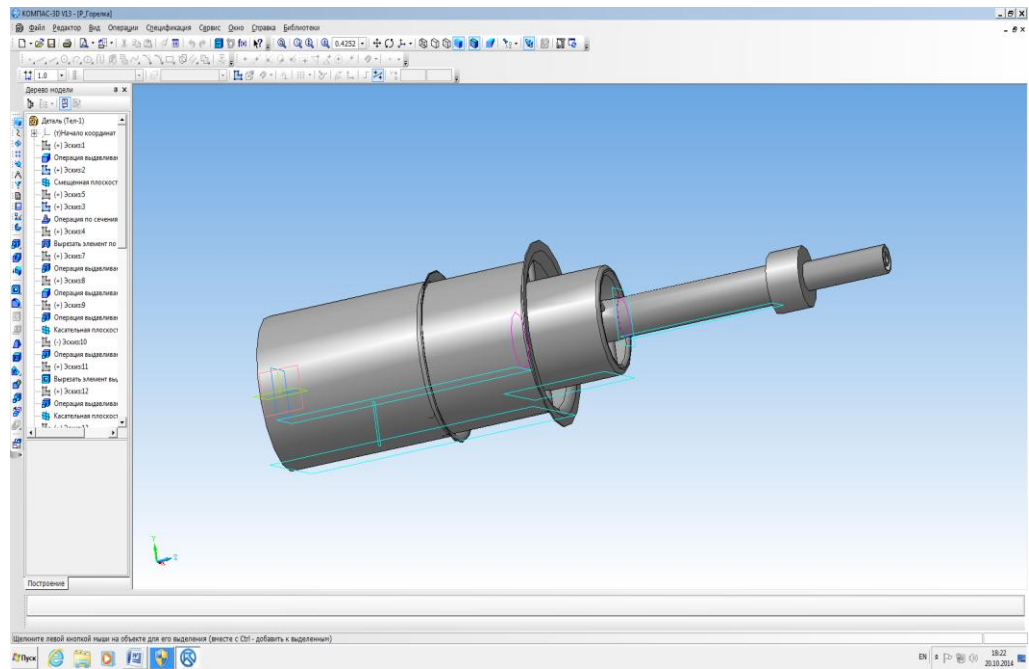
3D чертеж горелочного устройства (с оболочками)
